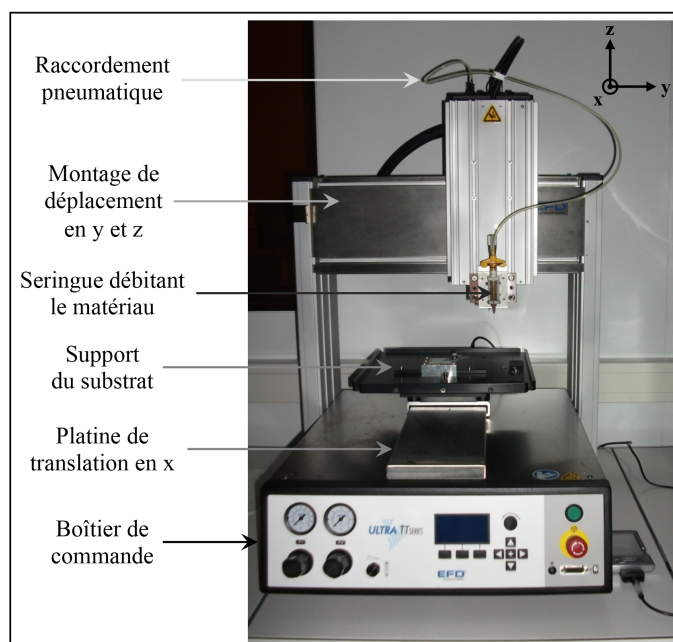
Machine de préformage utilisée pour le dépôt d'Ormocomp
